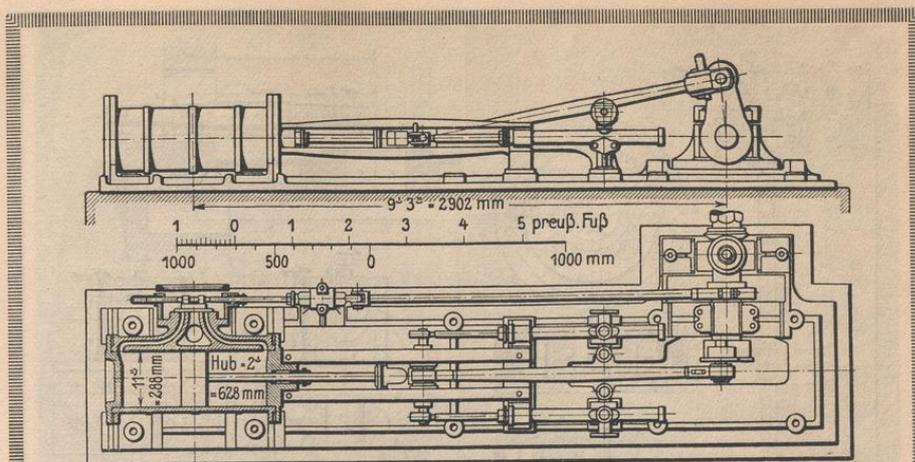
Liegende Schieberdampfmaschine der Maschinenfabrik Kamp & Co., erbaut um 1840.
